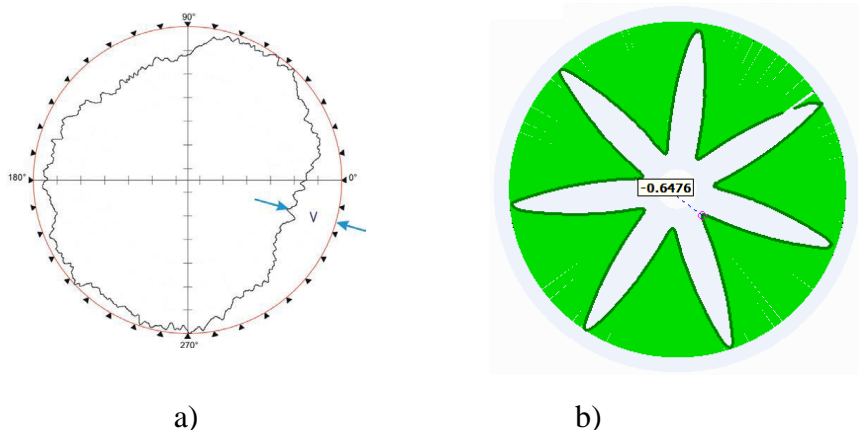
a) referenční kružnice minimální zóny kružnice [18], b) referenční kružnice minimální zóny kružnice 50 pence v softwaru InSpec
